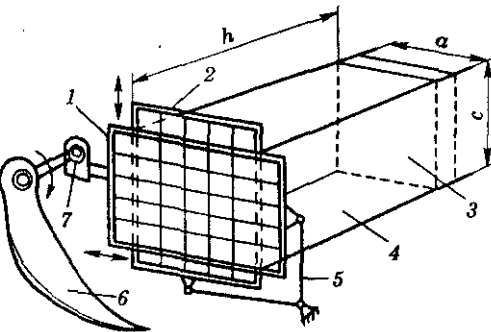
Функціональна схема шпигорізки: 1, 2 — рами з плоскими ножами; 3 — штовхач; 4 — приймальний короб; 5 — куліса; 6 — серпоподібний ніж; 7 — ексцентриковий механізм
